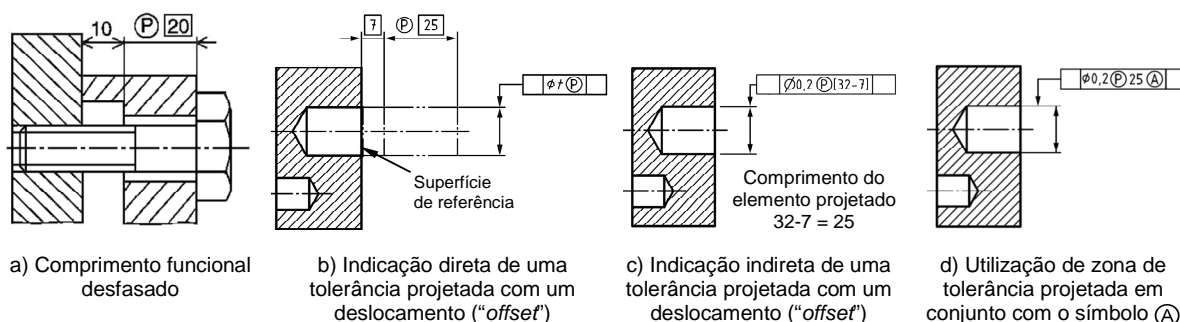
Exemplos de especificações de elementos toleranciados projetados. Adaptada do ISO/DIS 1101.2
